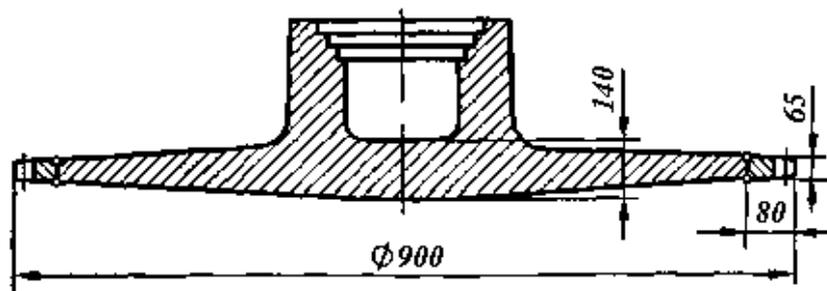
Сварной вариант ротора газовой турбины
